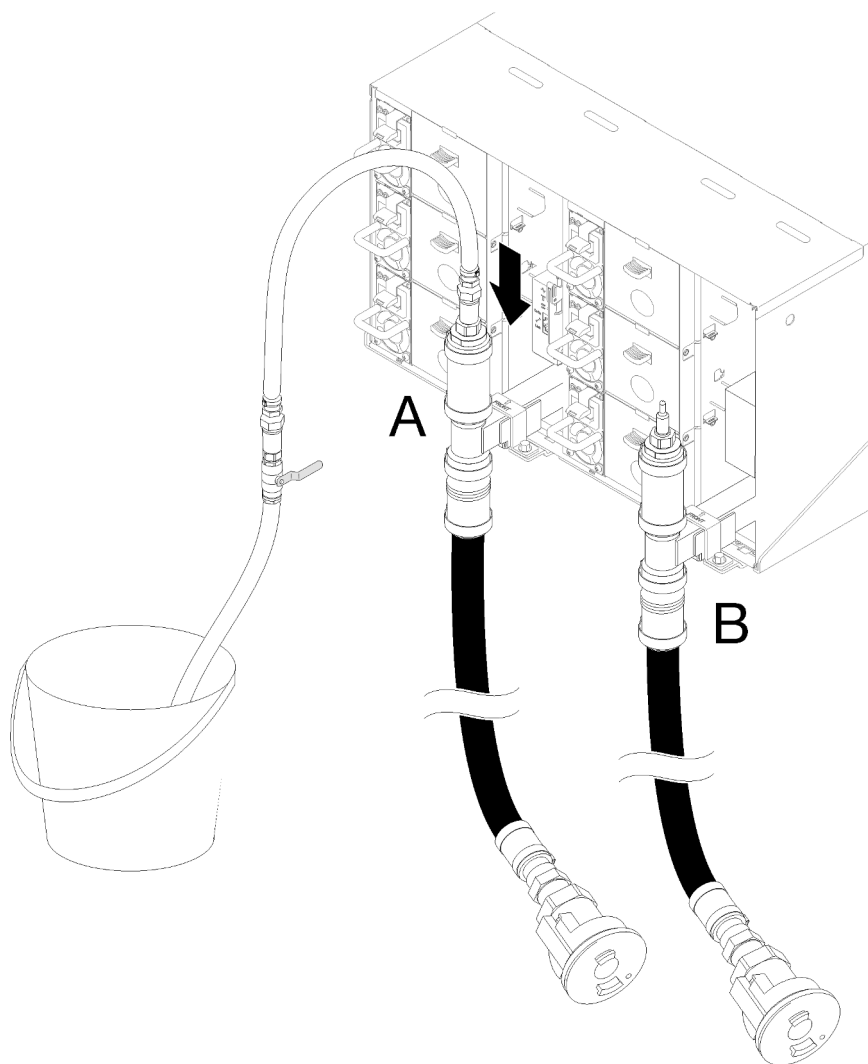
Collegamento dell'assieme del tubo blu al collegamento rapido superiore
